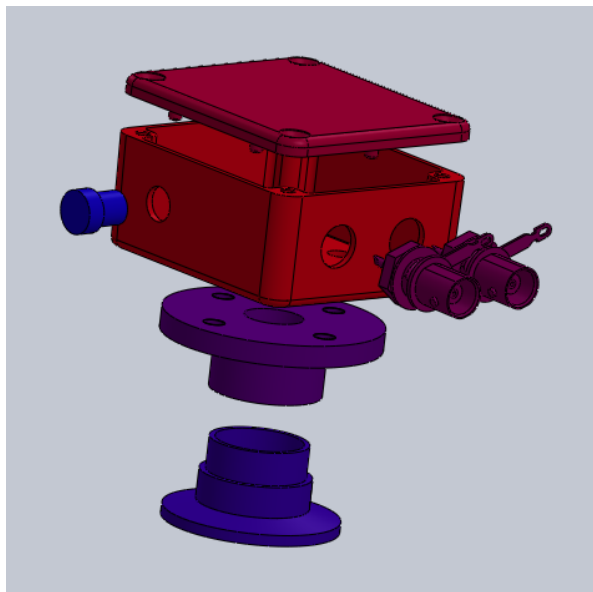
Explosionszeichnung des Drucksensorgehäuses
